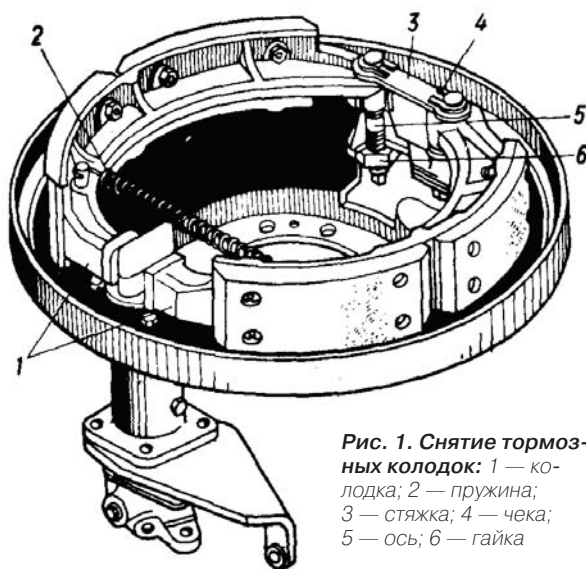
Снятие тормозных колодок: 1 — колодка; 2 — пружина; 3 — стяжка; 4 — чека; 5 — ось; 6 — гайка
